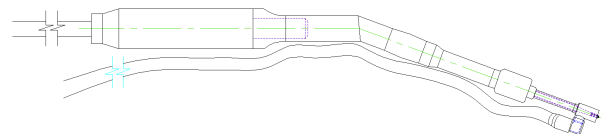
Vista del conjunto seccionador – sistema de aspiración (Boquilla - Cánula).
